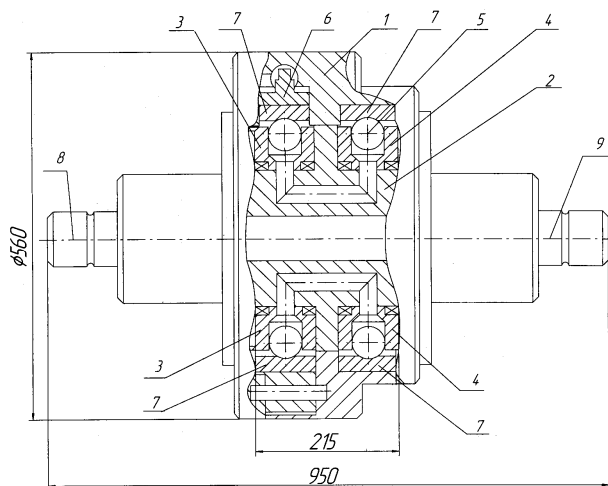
Гидропередача ГОП-900 с шариковыми поршнями [26]:
